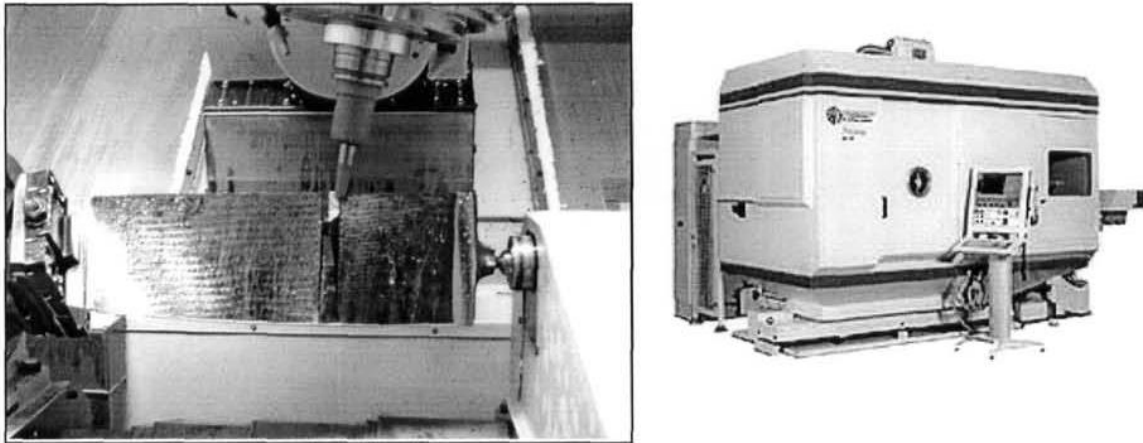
Пяти-координатный фрезерный центр НХ-151
